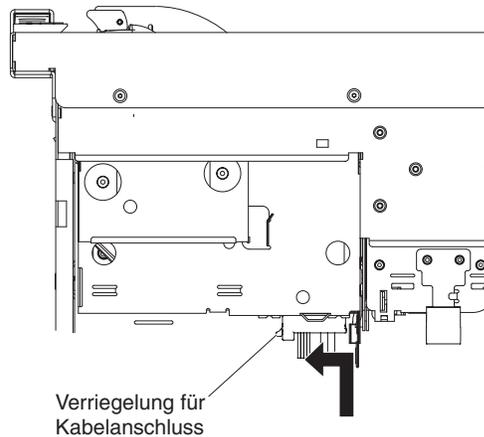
Sperre für Kabel des DVD-Laufwerks
